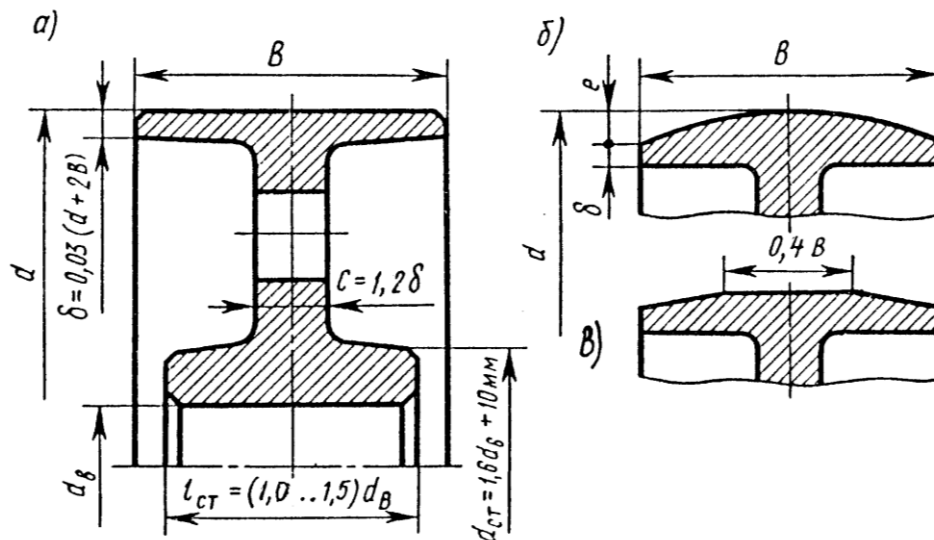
Размеры шкивов плоскоремennых передач:
